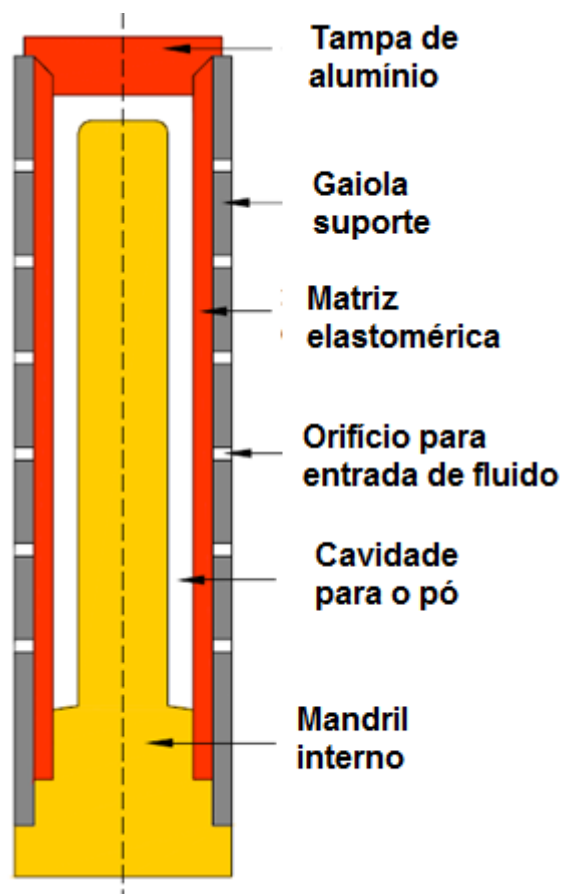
Esquema de molde tubular utilizado neste trabalho.
